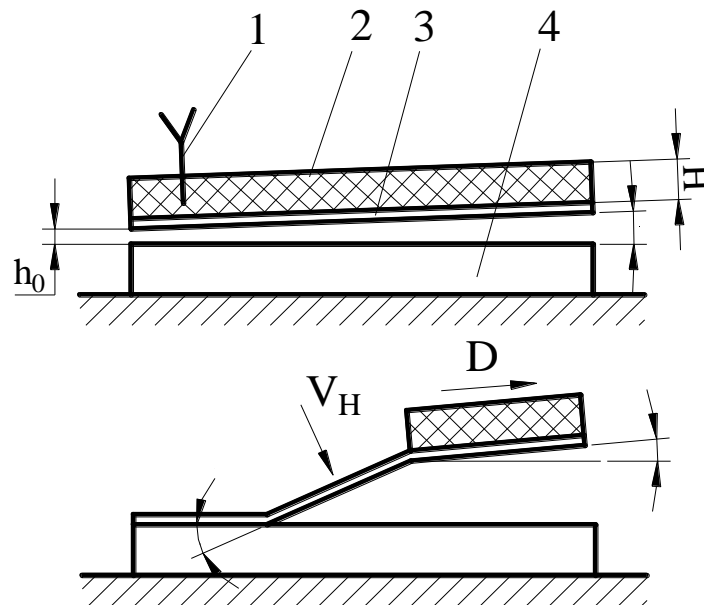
Схема сварки взрывом: 1 — детонатор; 2 — взрывчатое вещество; 3, 4 — свариваемые заготовки;  $D$  — скорость детонации;  $V$  — нормальная скорость метаемой пластины
